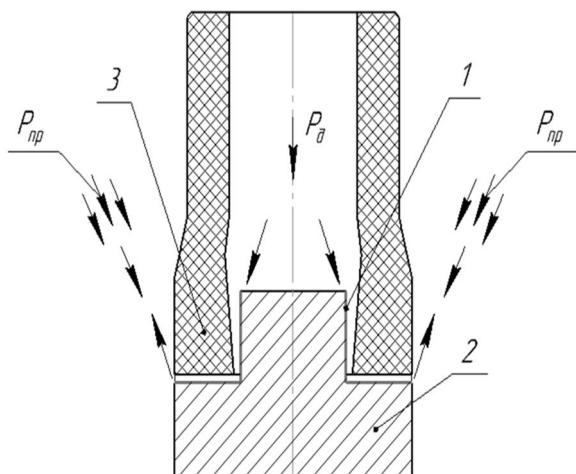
Схема формоутворення чистової обробки по зовнішньому контуру
